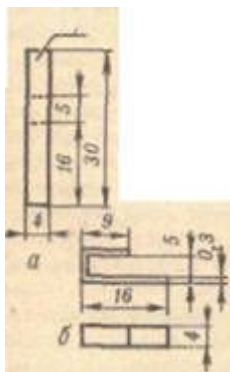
Лепесток: а — заготовка, б готовое изделие.
